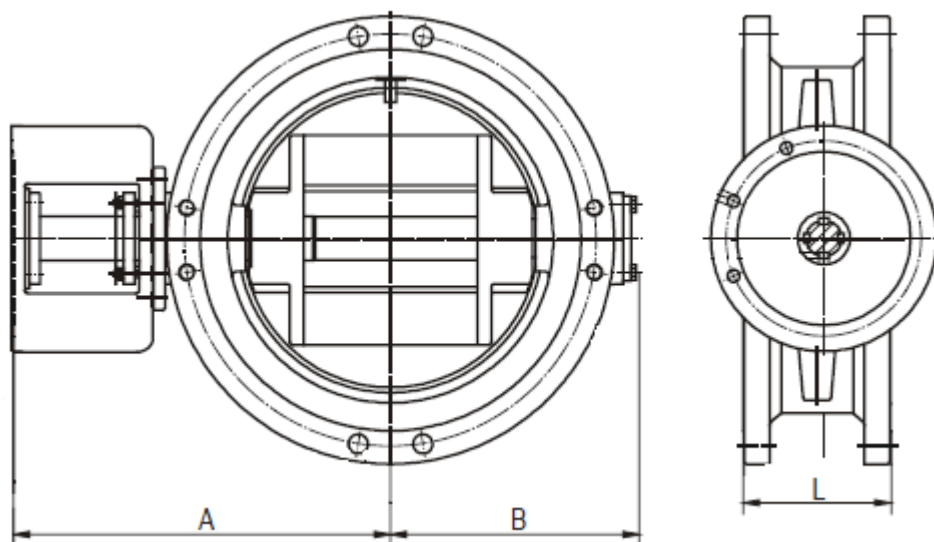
Габаритные размеры затвора дискового МАК-16.
